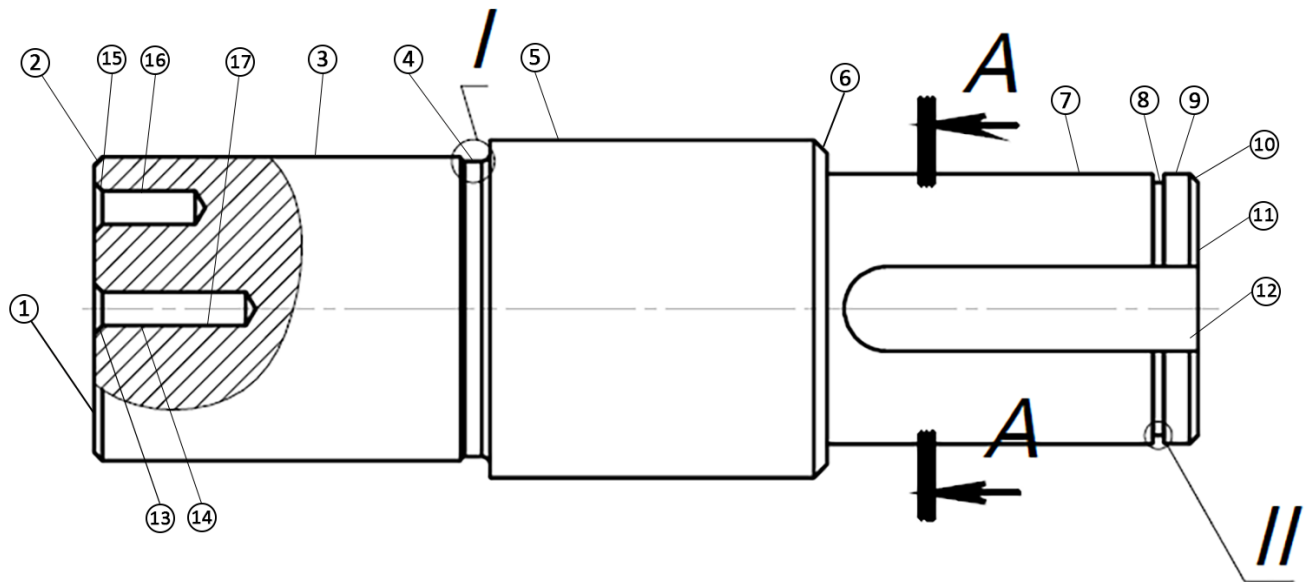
Нумерація поверхонь деталі “Вал”
